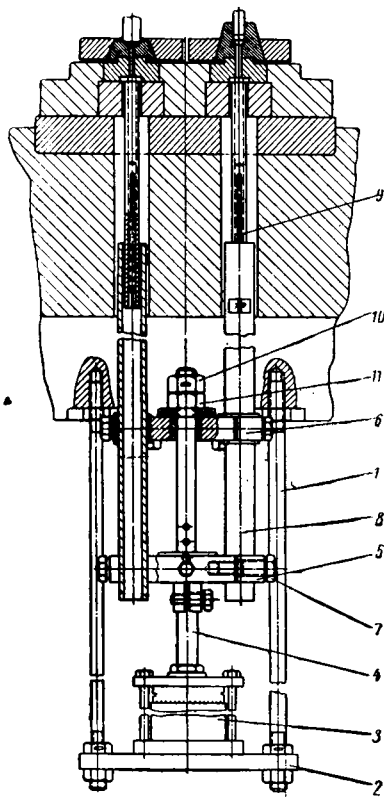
Устройство пневматического выталкивающего устройства, применяемого на МЗМА.
